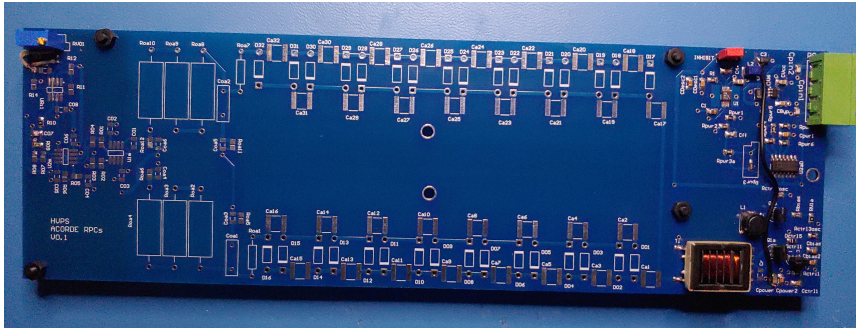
Placa de la HVPS, con los componentes iniciales ya soldados, del lado derecho se puede ver el puente.
